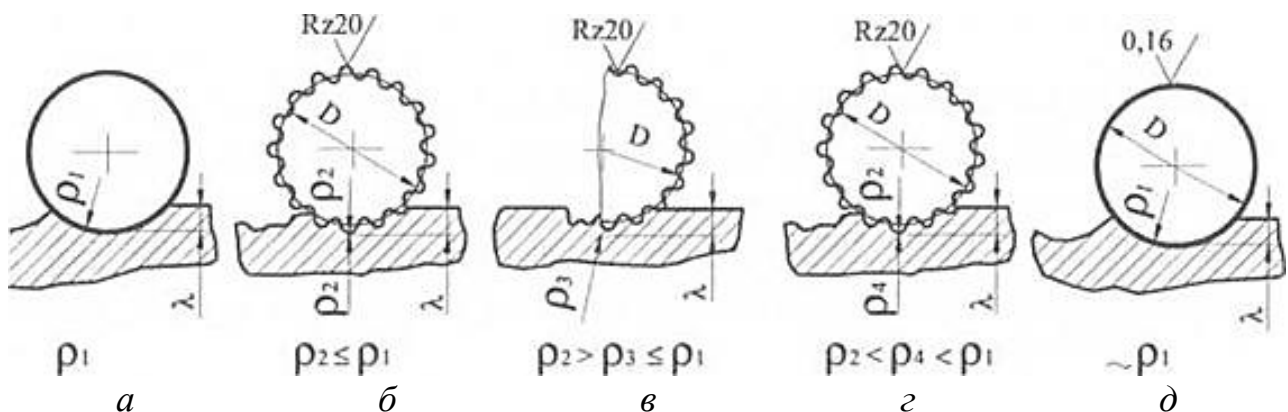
випадки зони контакту з поверхнею деталі (твердість дробинки вище, ніж у деталі): а – ідеальна куля; б, г – чавунний або сталевий литий дріб цілий; в – чавунний литий дріб розколотий; д – кулька від підшипника; а, б, в – сухий удар; г, д – удар через змащувально-охолоджувальну рідину.
